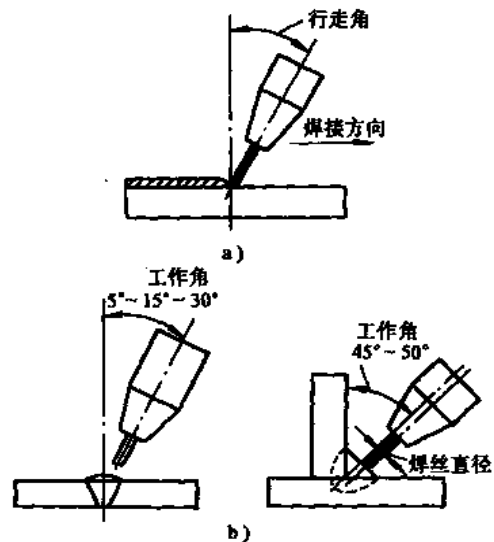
焊丝相对于焊接方向和焊缝轴线的行走角和工作角
